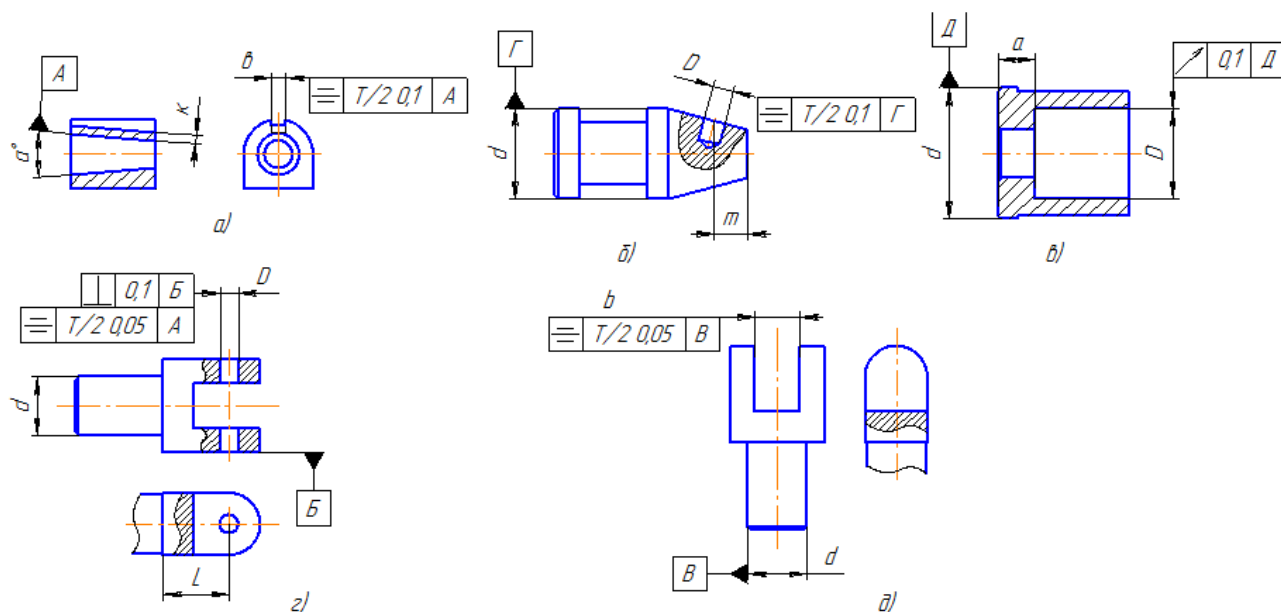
Обрабатываемые заготовки к задаче 1.1
